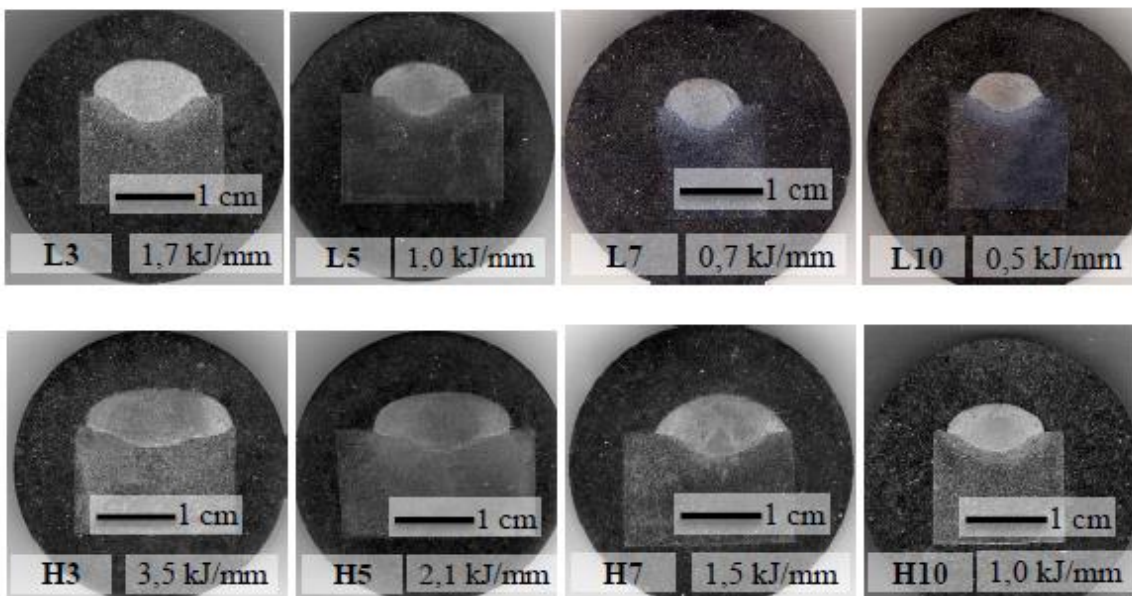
Macroestructuras de las probetas soldadas sin protección gaseosa
